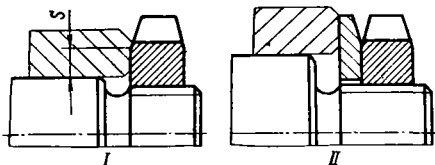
Установка кольцевой гайки без шайбы (I) и с шайбой (II)
